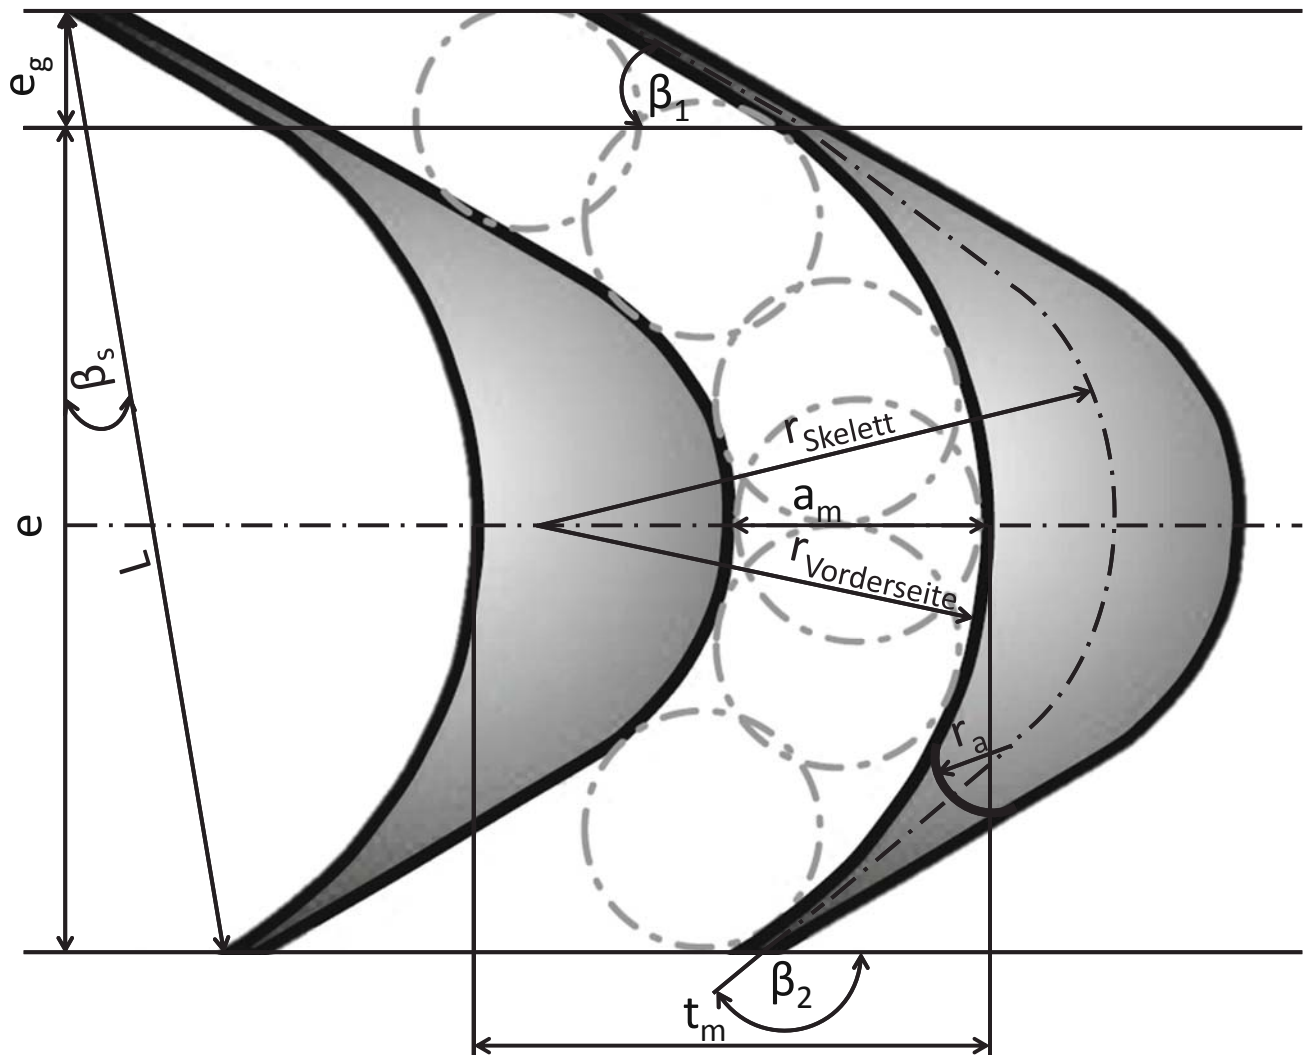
Schaufelgeometrie des Laufrades einer axialen Gleichdruck-Turbine am mittleren Durchmesser d_m
